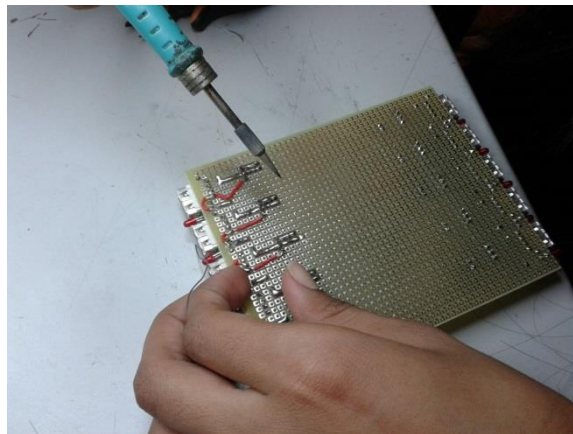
Proceso de fabricación del cargador: Soldaduras
